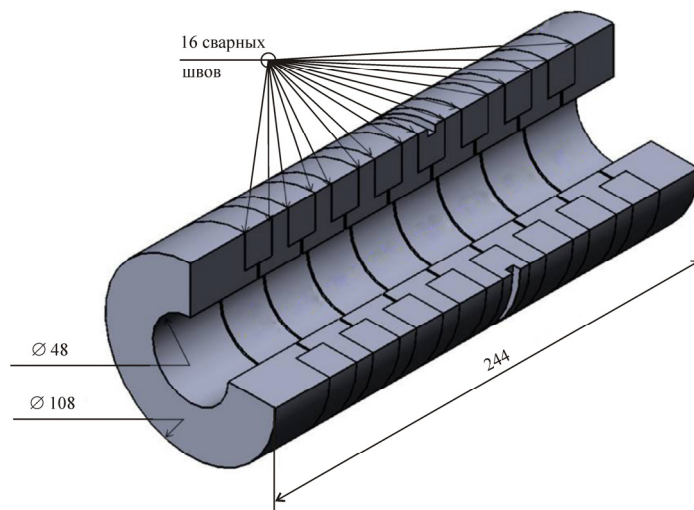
Конструкция сварного комбинированного магнитопровода электрической машины (разрез 3/4)
